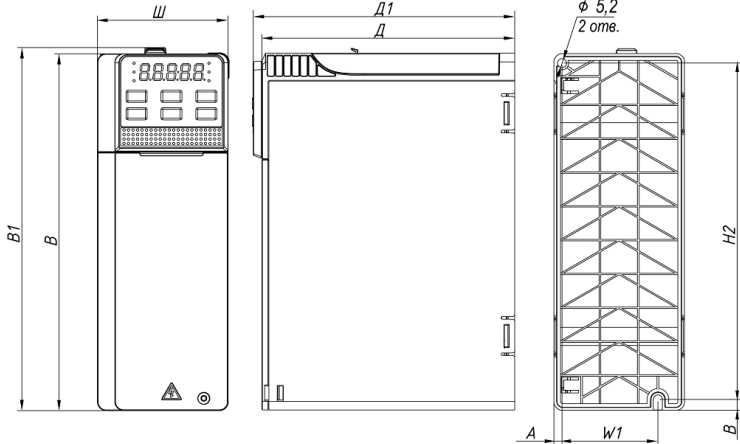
Габаритные и присоединительные размеры (типоразмер 2)
